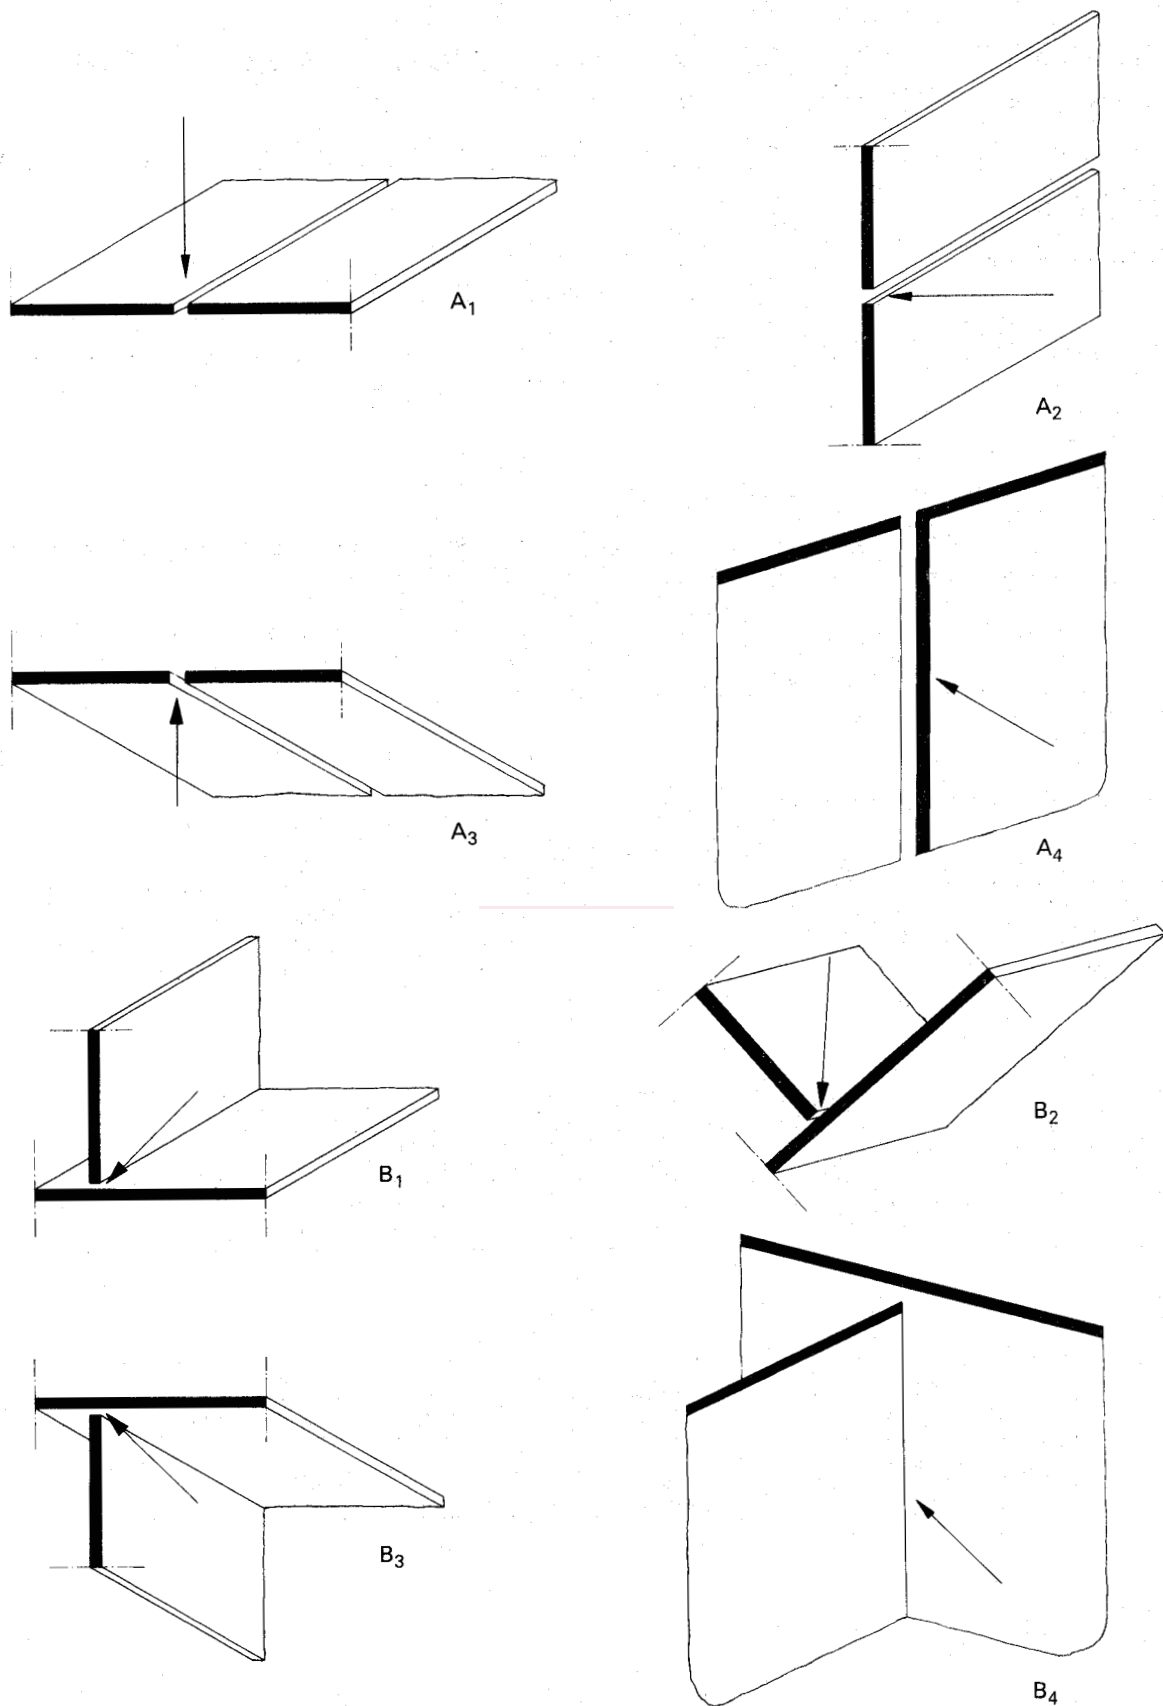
Positions fondamentales d'exécution des soudures
